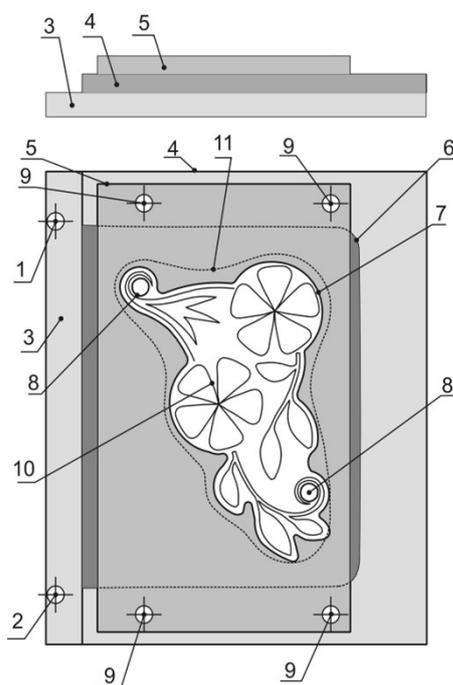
Схема конструкции технологической кассеты для автоматизированной сборки клапана женской сумки:
